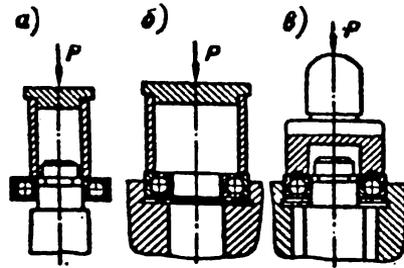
Установка подшипников качения: а – на вал; б – в корпус; в – одновременно на вал и в корпус
